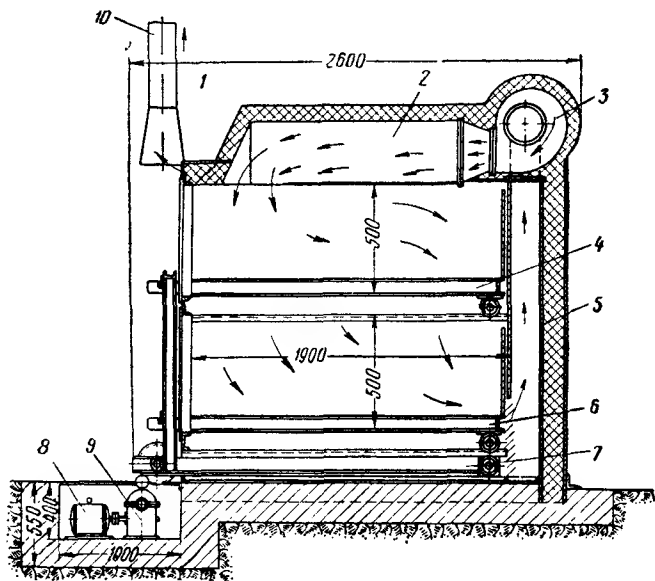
Общий вид электрической печи для нагревания коллекторов: 1 — вытяжная вентиляция; 2 — электрокалорифер; 3 — вентилятор; 4 — прицепная тележка (верхняя); 5 — каркас; 6 — прицепная тележка (нижняя); 7 — ведущая тележка; 8 — электродвигатель; 9 — редуктор; 10 — вентиляционное устройство
